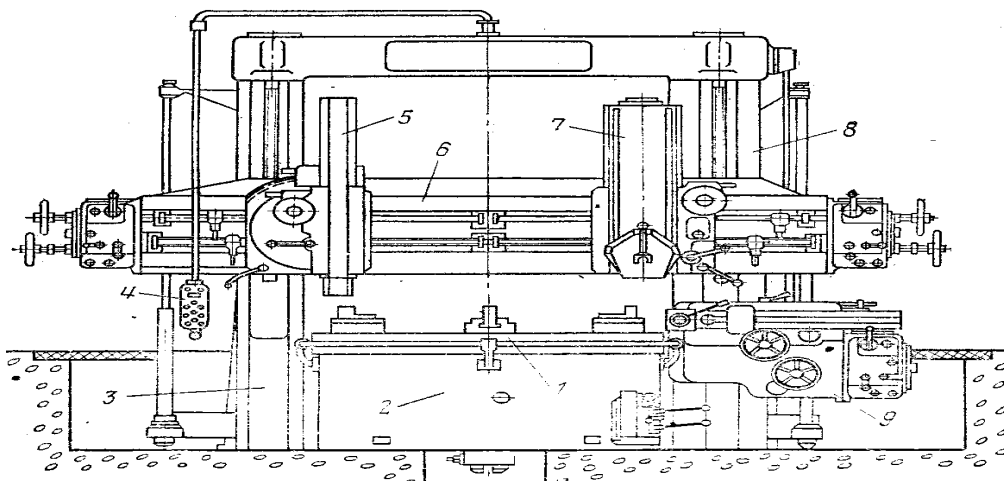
Загальний вигляд токарно-карусельного верстату.
